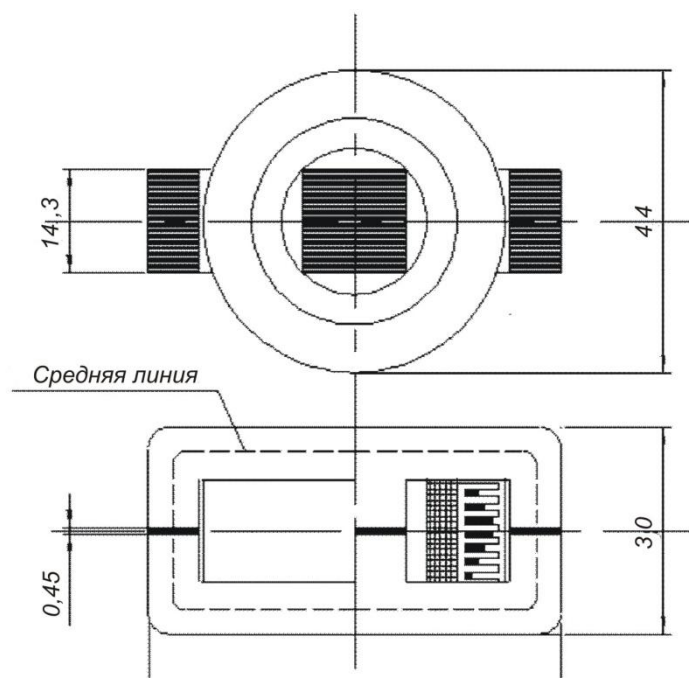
Сборочный и габаритный чертежи катушки: сверху – вид со стороны торца обмоток; внизу - сечение обмоток и общий вид сердечника
